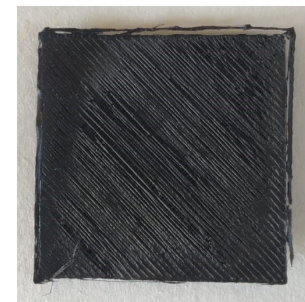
Placa impresa boq.0,4mm, ep=1,4mm
